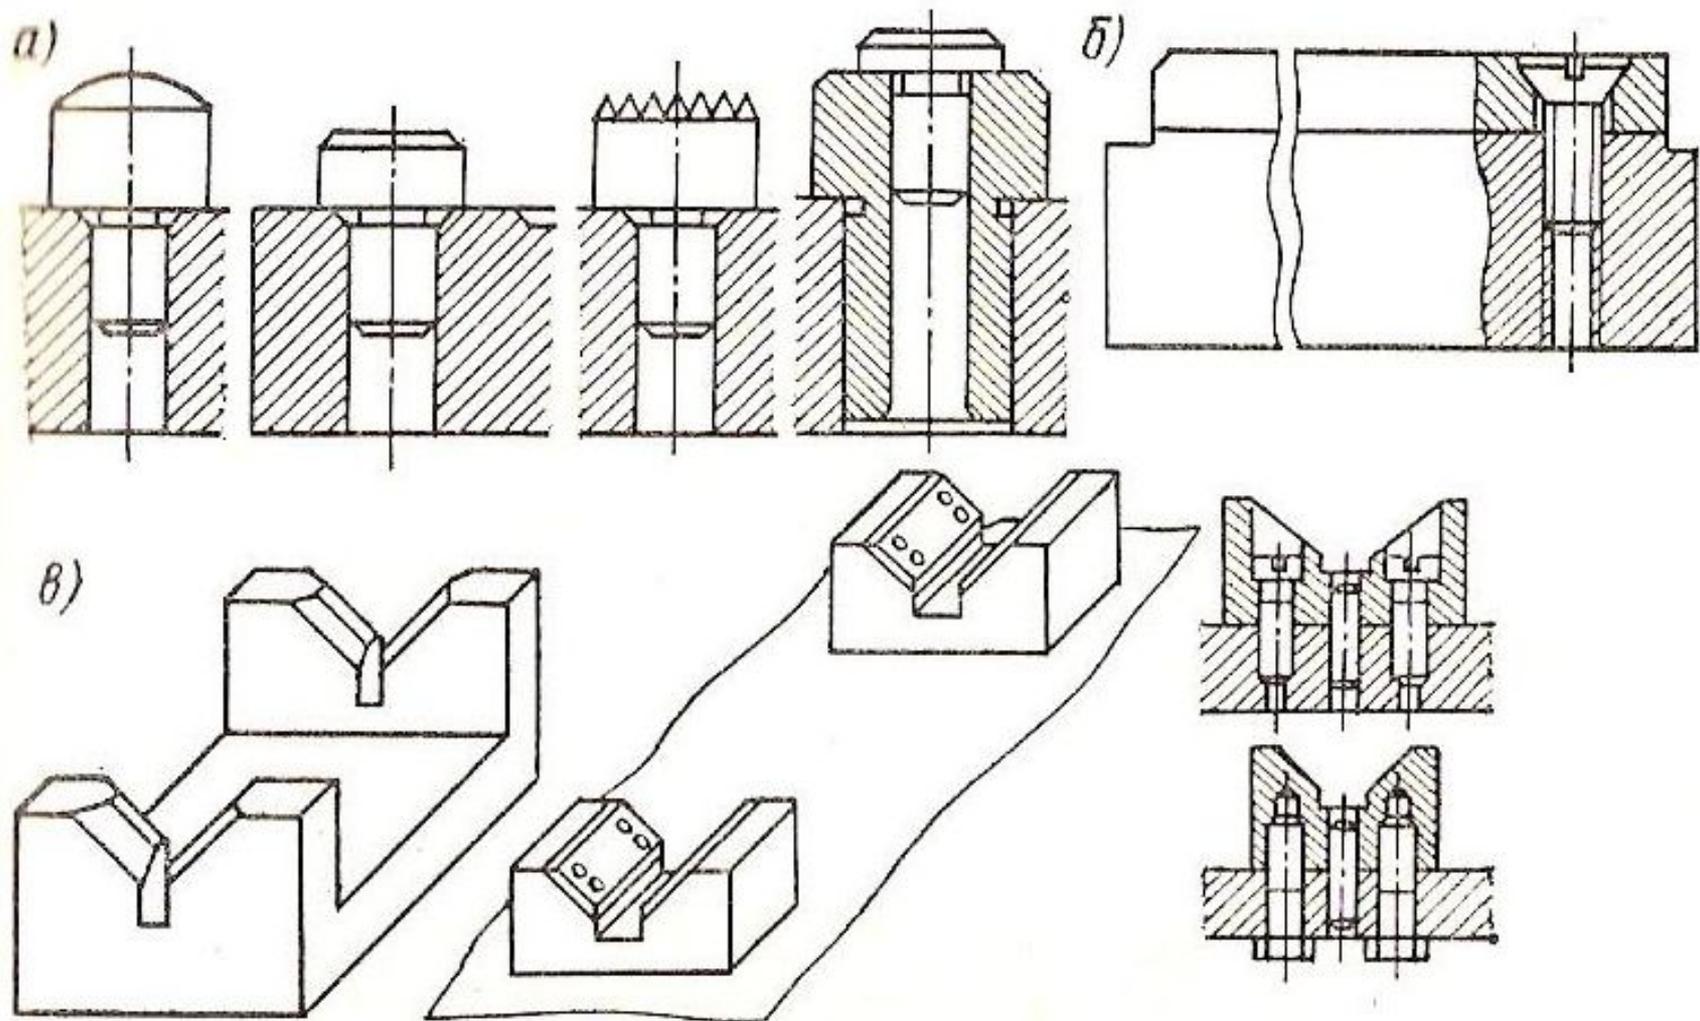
Виды установочных неподвижных опор: а - штыри; б - пластины; в - призмы.
